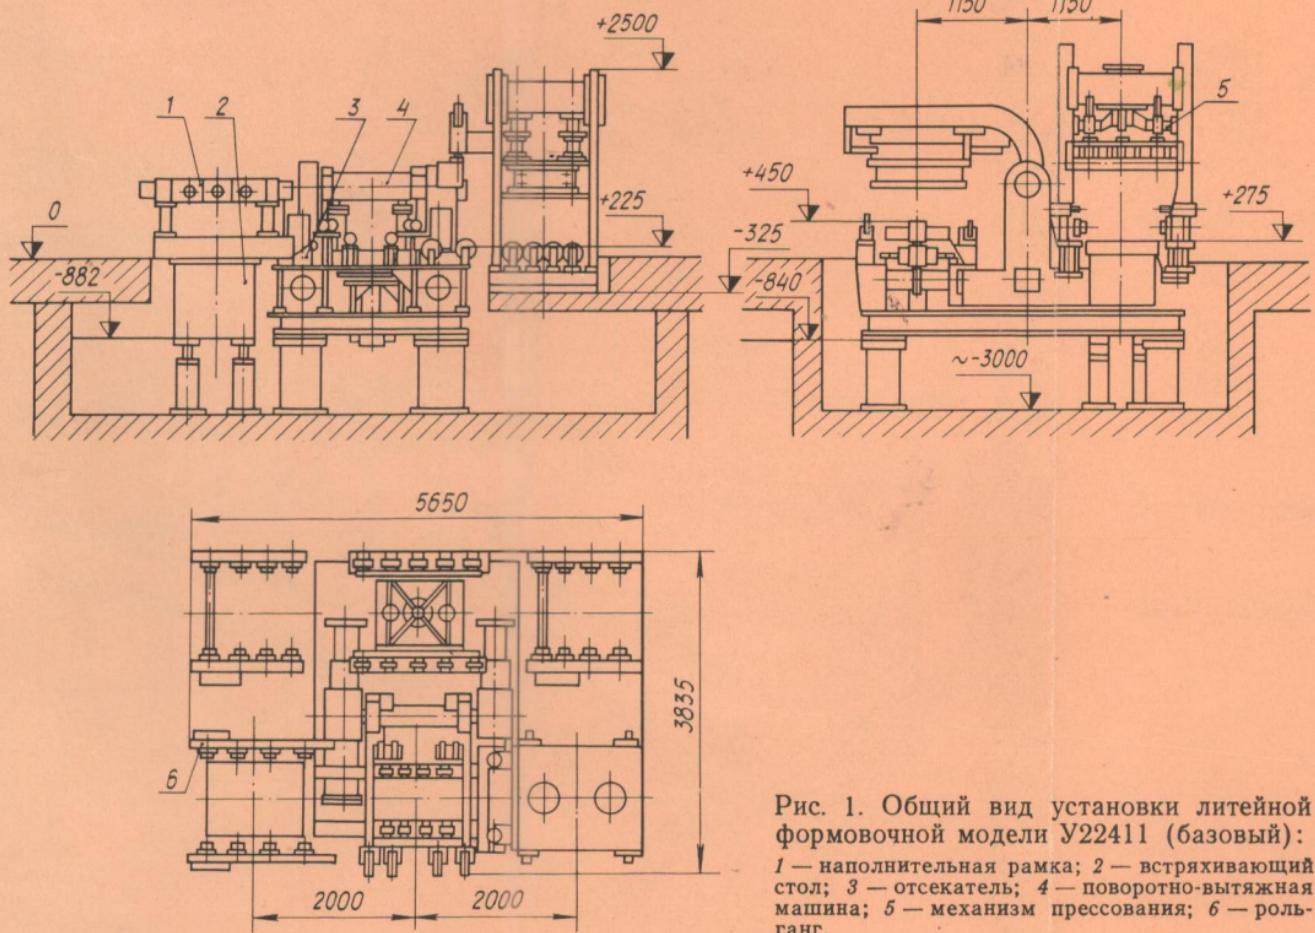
Общий вид установки литейной формовочной модели У22411 (базовый):
